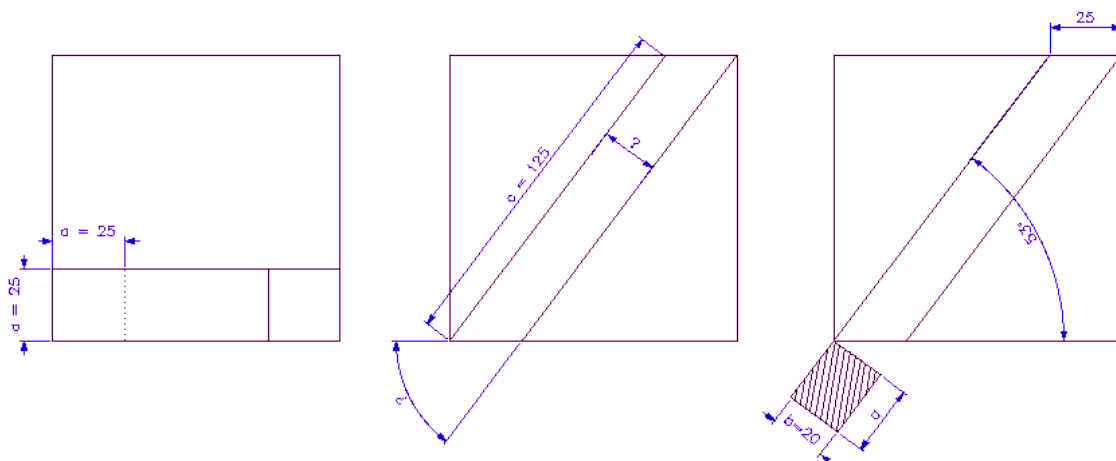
Im Grundriss (Links) und Aufriss (Mitte, rechts) sind Längen und Winkel des Prismas in der Abbildung nicht verzerrt.
